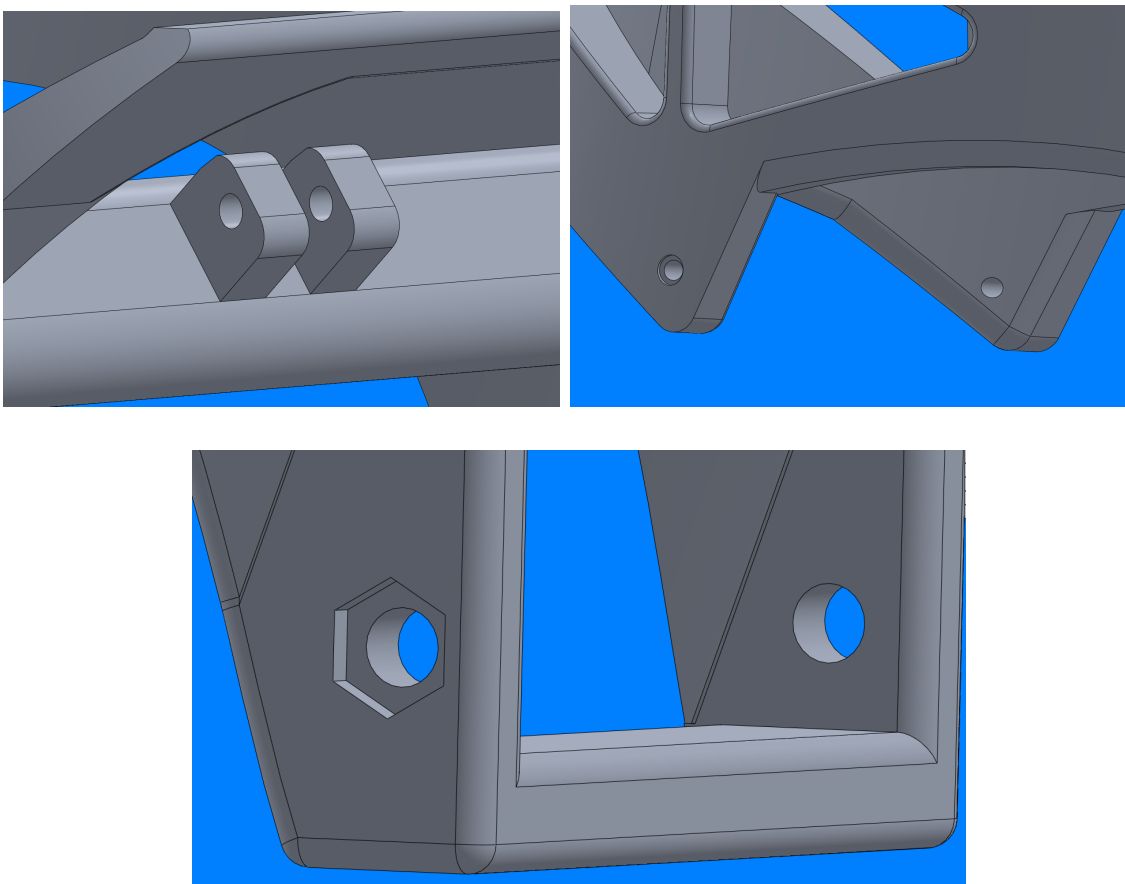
Vistas detalle anclajes suspensión, basculante y motor
